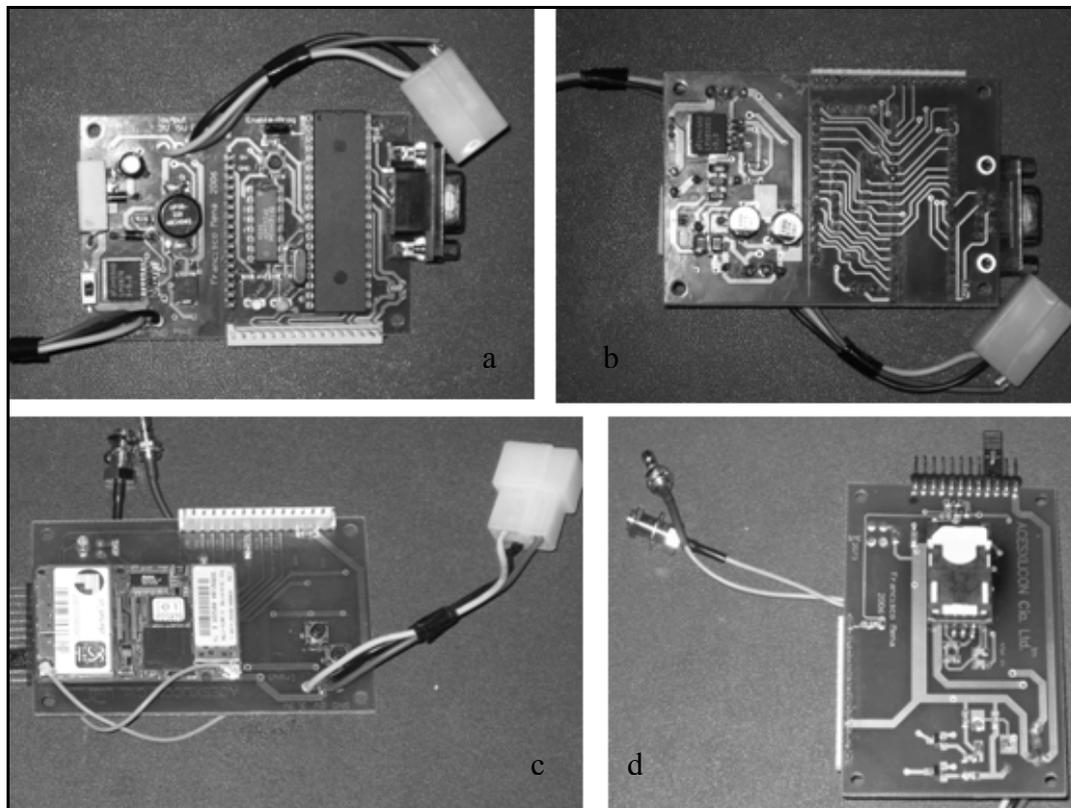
Tarjetas PCB del Sistema Móvil. a) Cara Superior PCB Fuente/Controlador. b) Cara Interior PCB Fuente/Controlador. c) Cara Superior PCB Comunicaciones d) Cara Inferior PCB Comunicaciones
